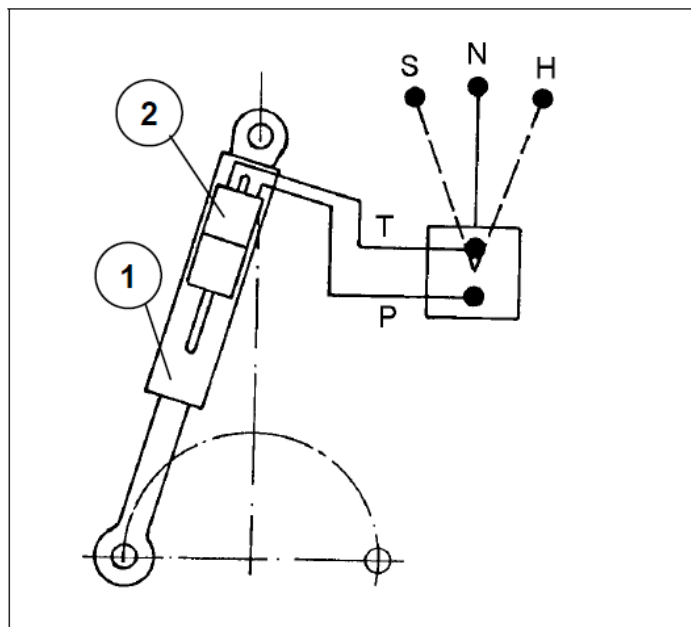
Схема роботи поворотного циліндра обертання рами
